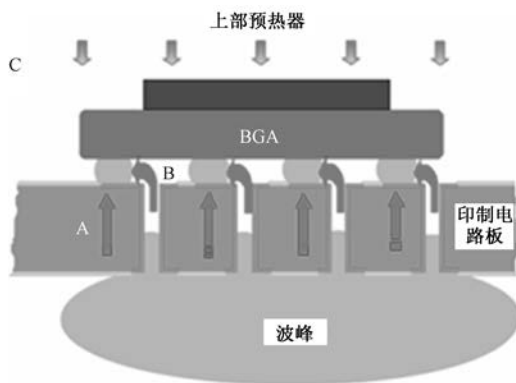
在波峰焊接过程中对 PCB 上表面 BGA 焊点的加热路径
